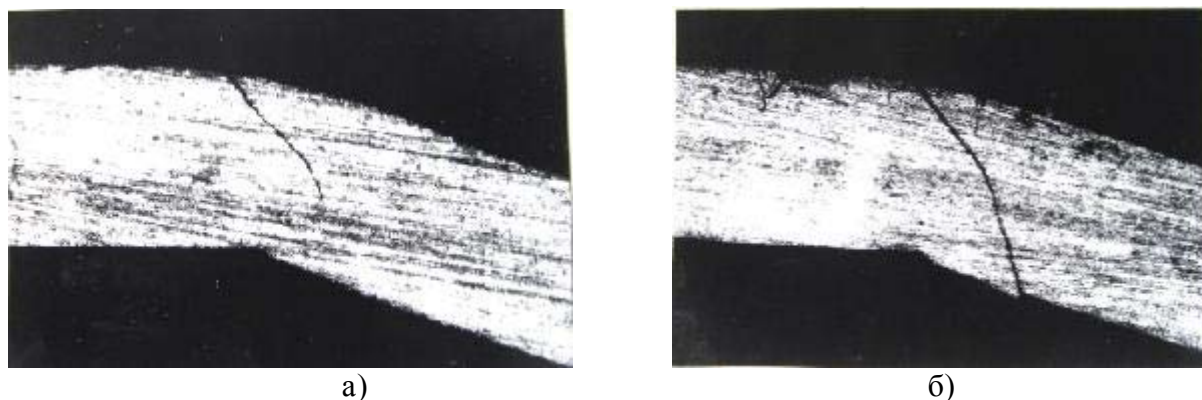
Стадии разрушения материала заготовки в очаге разделения по классической схеме вырубki детали полиуретаном (x20)
